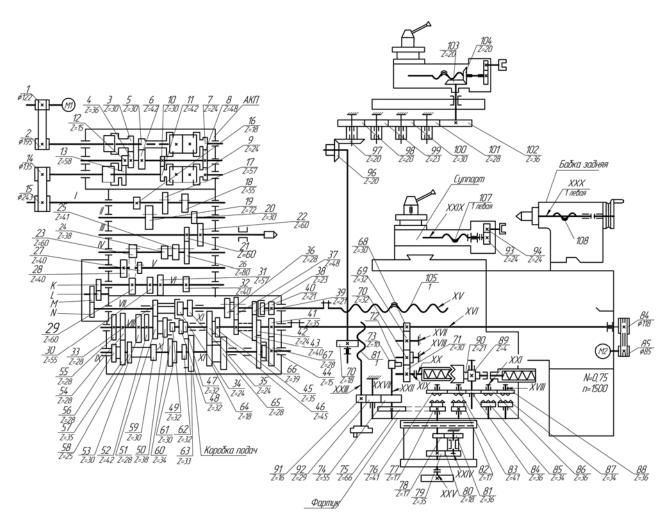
Кинематическая схема станка модели 16Д25
